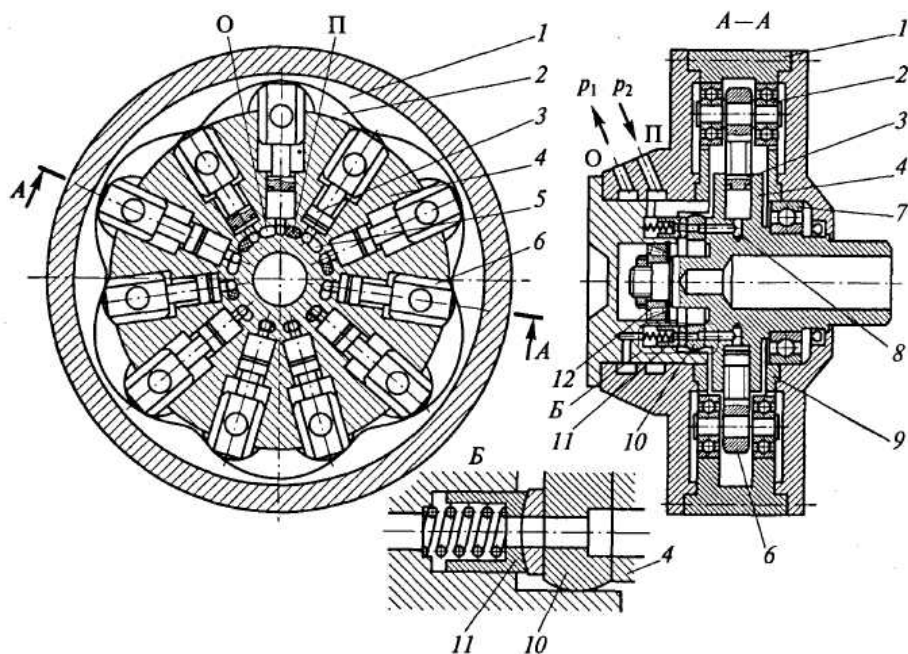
Радиально-поршневой гидромотор многократного действия (высокомоментный гидромотор): 1 – статор; 2 – опора качения роликов; 3 – поршень; 4 – блок цилиндров; 5 – дуговое окно; 6 – ползун; 7, 12 – подшипники; 8 – канал; 9 – контрнаправляющий кулачок; 10 – торцовый распределитель; 11 – стакан; О – камера отвода; П – камера подвода;  $p_1$  – давление отвода;  $p_2$  – давление подвода
